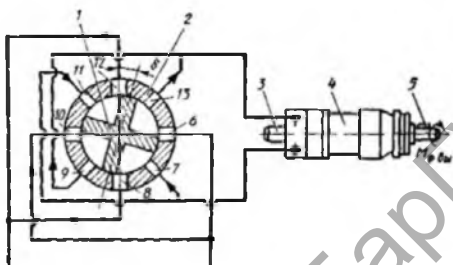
Схема соединения шагового двигателя с гидросистемой
